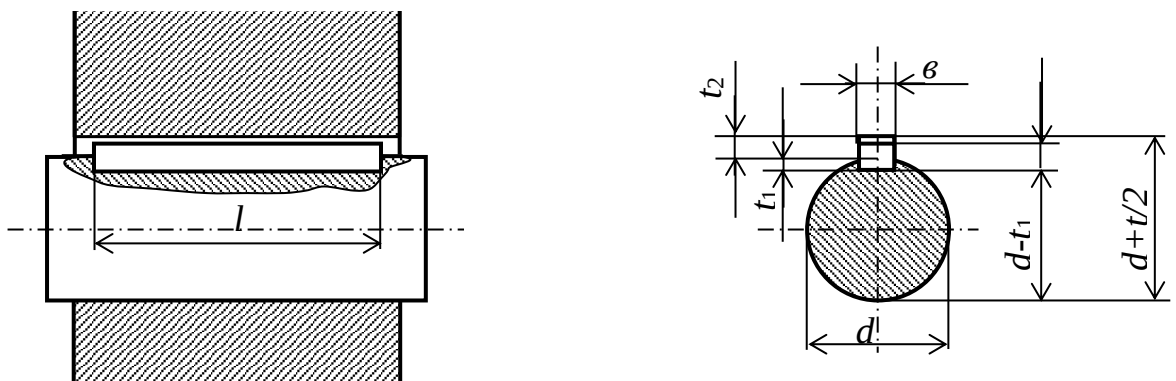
Схема для розрахунку шпонкового з'єднання
